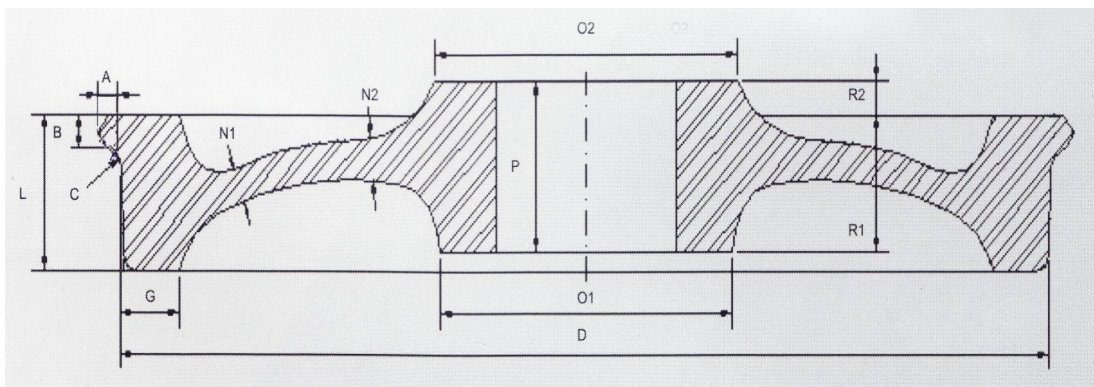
Desenho esquemático do corte de uma roda de locomotiva
